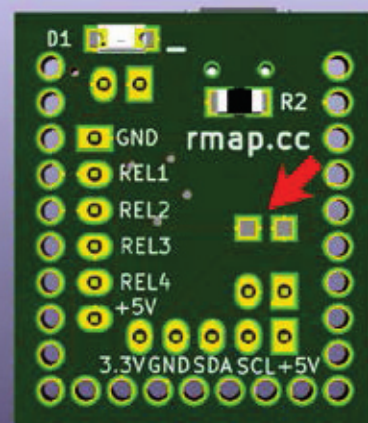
Le piazzole SET sono dal lato saldature della board STIMA-I2C.
